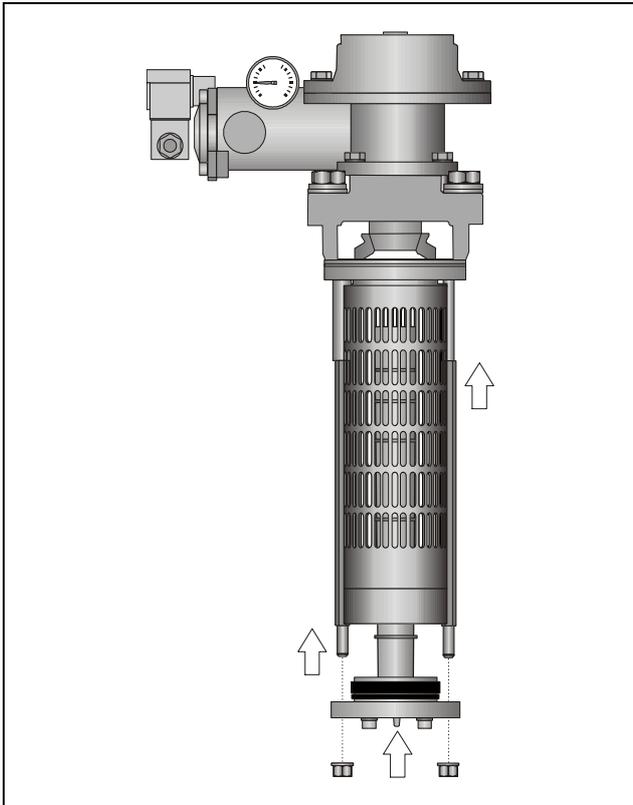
Vormontierte Baugruppe in Antriebswelle einfügen
